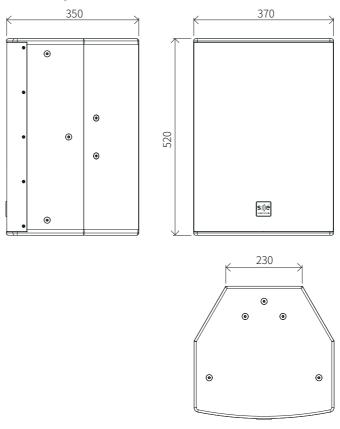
COX 12 MKII Ansichten und Abmessungen. Angaben in Millimetern.
